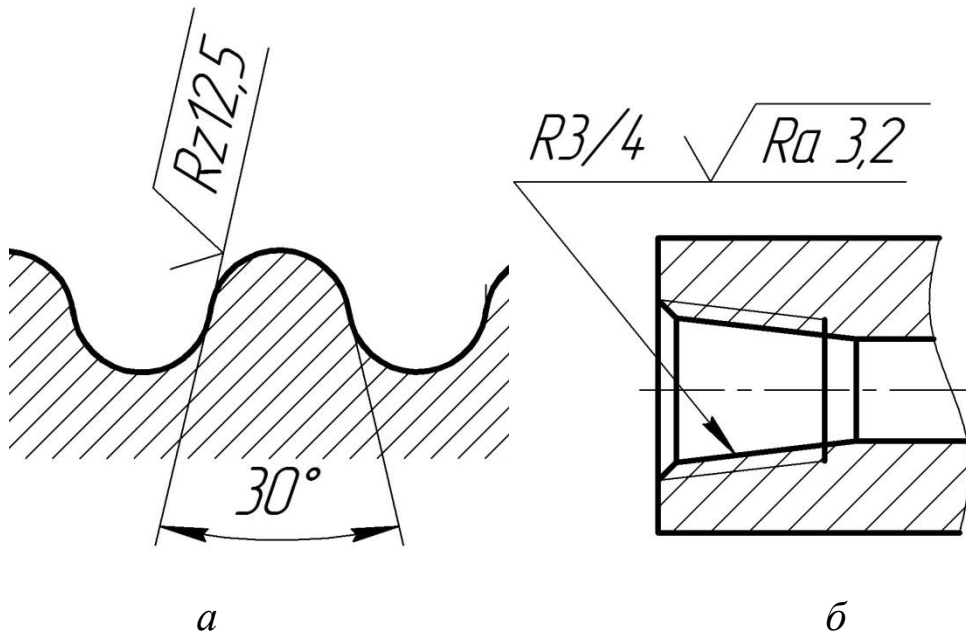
Обозначение шероховатости поверхности профиля резьбы (а) и резьбы (б)
